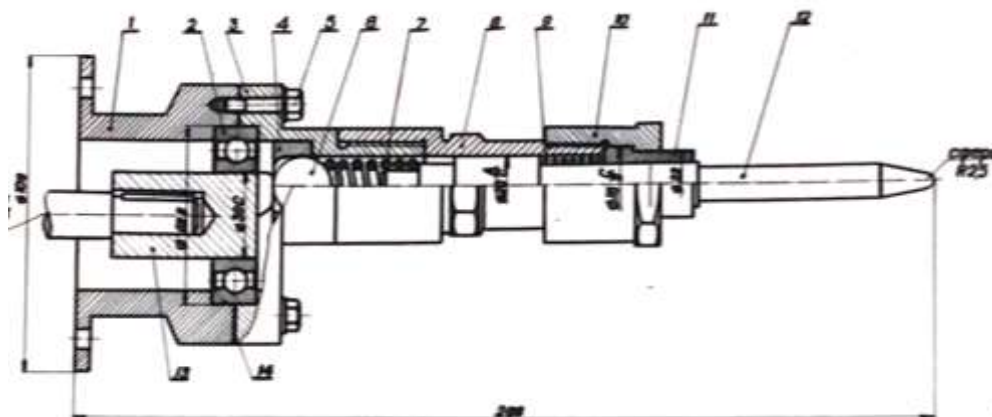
Конструкція пристосування для карбування: 1 – корпус, 2 – підшипник, 3 – кришка, 4 – втулка, 5 – болт, 6 – кулька, 7 – пружина амортизаційна, 8 – втулка напрямна, 9 – пружина поворотна, 10 – гайка, 11 – втулка, 12 – ударник, 13 – прокладка, 14 – ексцентрикова втулка
